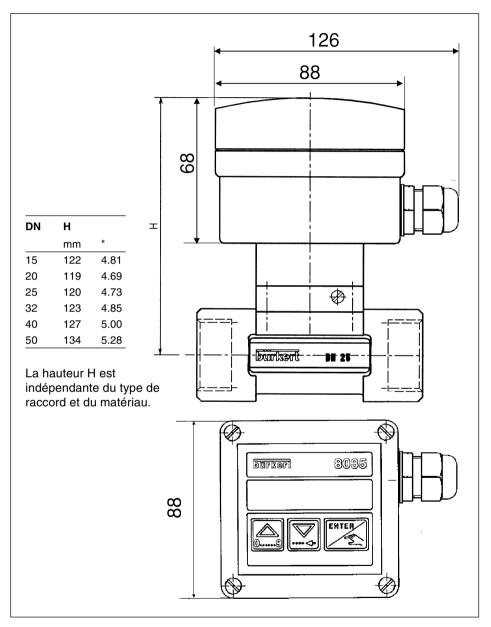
Transmetteur électronique 8035 dimensions externes
